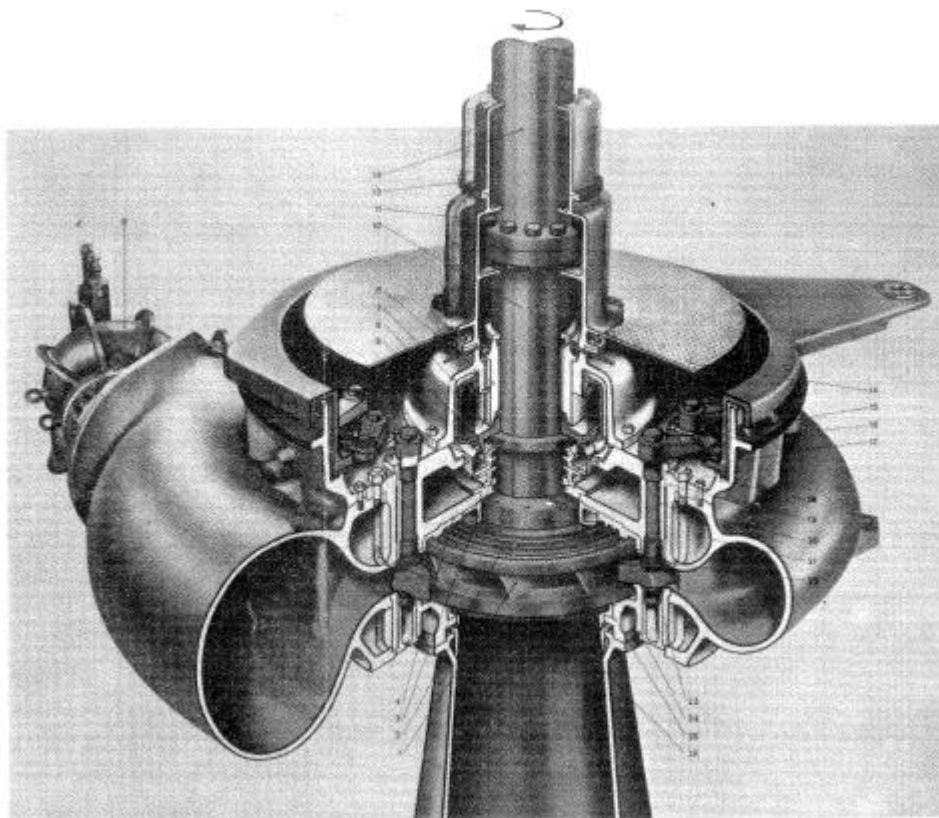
Corte en perspectiva de una turbina Francis junto con los elementos que la componen.
